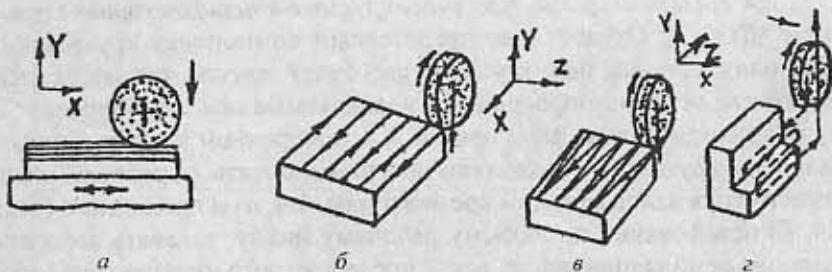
Схемы обработки плоских поверхностей на станках с ЧПУ
